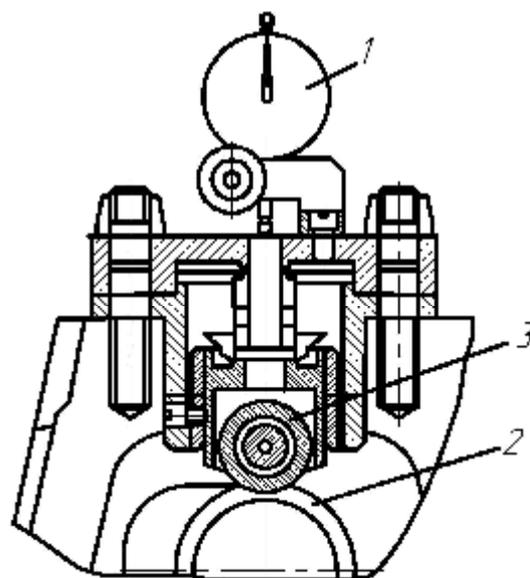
Приспособление для проверки общего угла опережения подачи топлива: 1 – индикатор часового типа; 2 – кулачок распределительного вала; 3 – ролик приспособления
